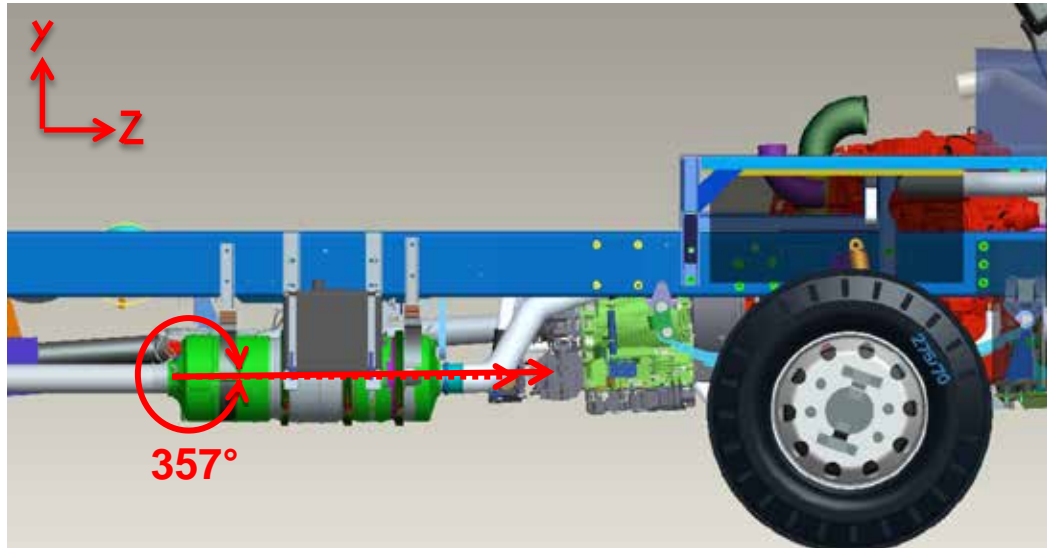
Inclínación del dispositivo de módulo único en posición de montaje, con respecto al eje horizontal. Diseño realizado en Pro/ENGINEER.
